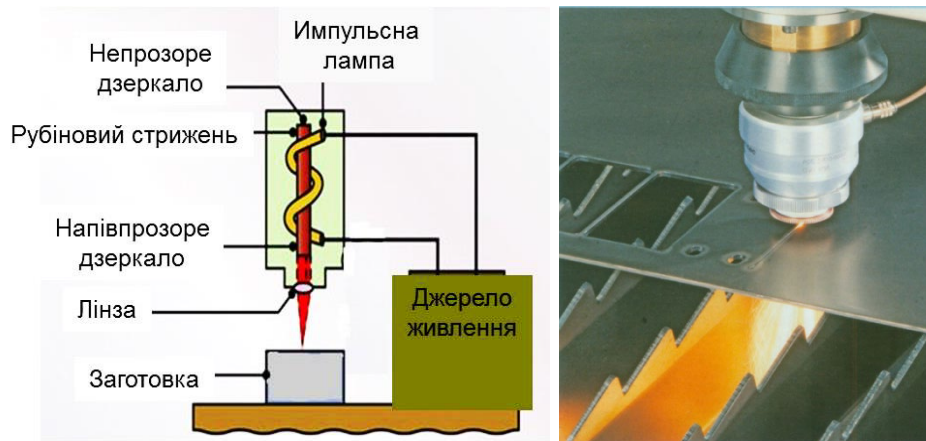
Схема лазерної обробки (а) і процес різання листового металу лазерним розкрійним комплексом (б).
